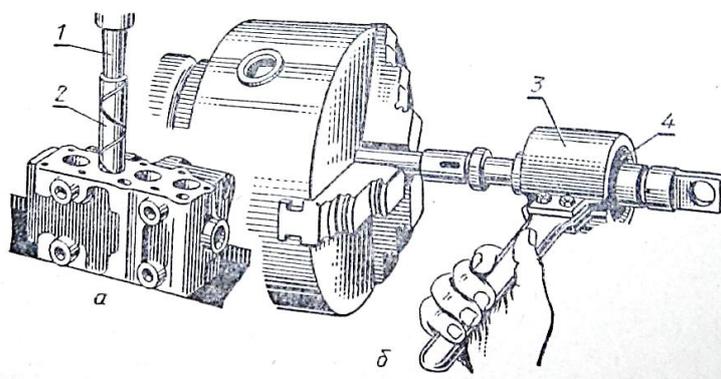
Ремонт золотника и корпуса распределителя:
